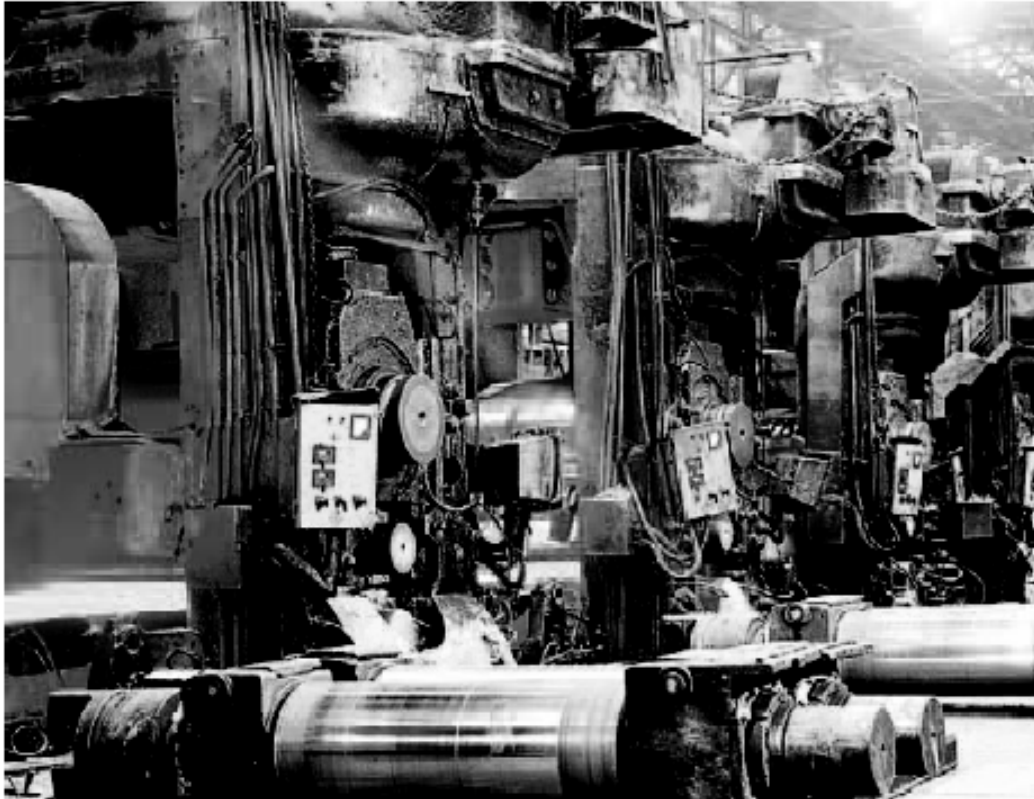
Неперервний стан гарячого прокатування 1680
